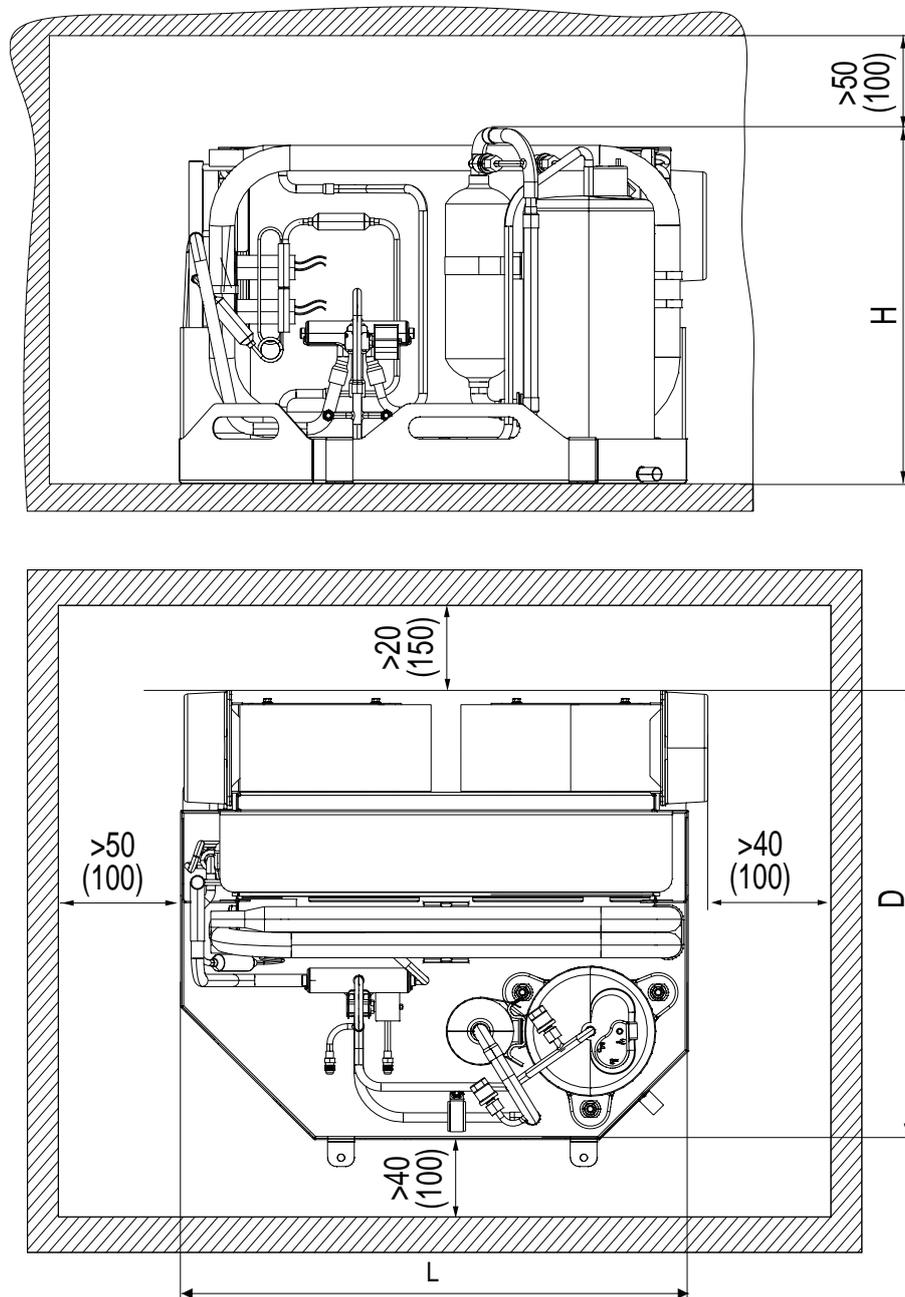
Abmessungen und Mindestabstände Typ S27 (mm)
